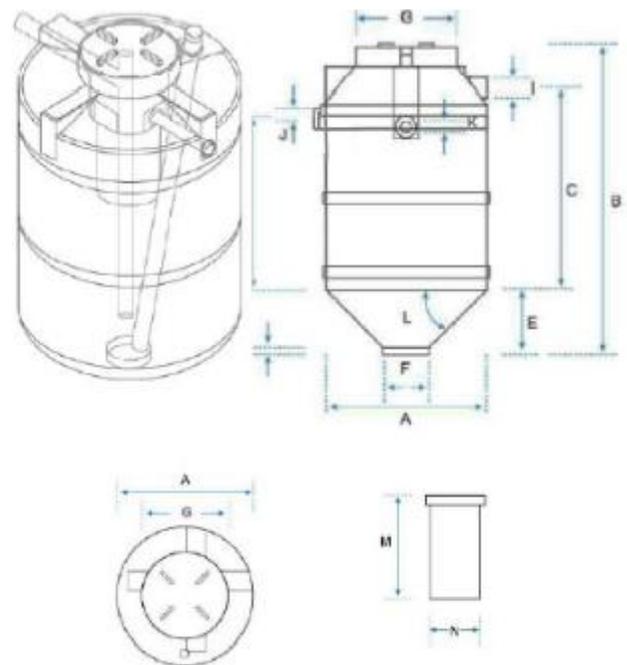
dimensiones del biodigestor(fuente guía de fabricantes)
